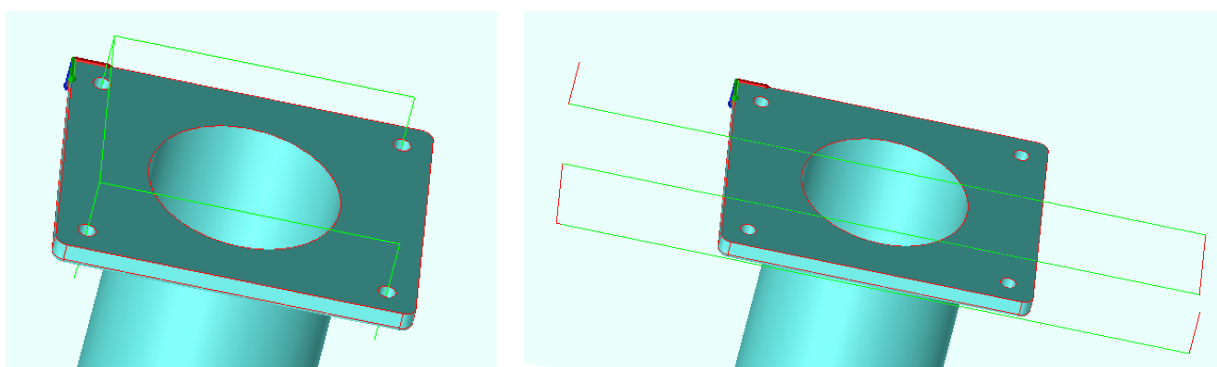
Dráhy nástrojů pro obrobení a vrtání prvního čela součásti
